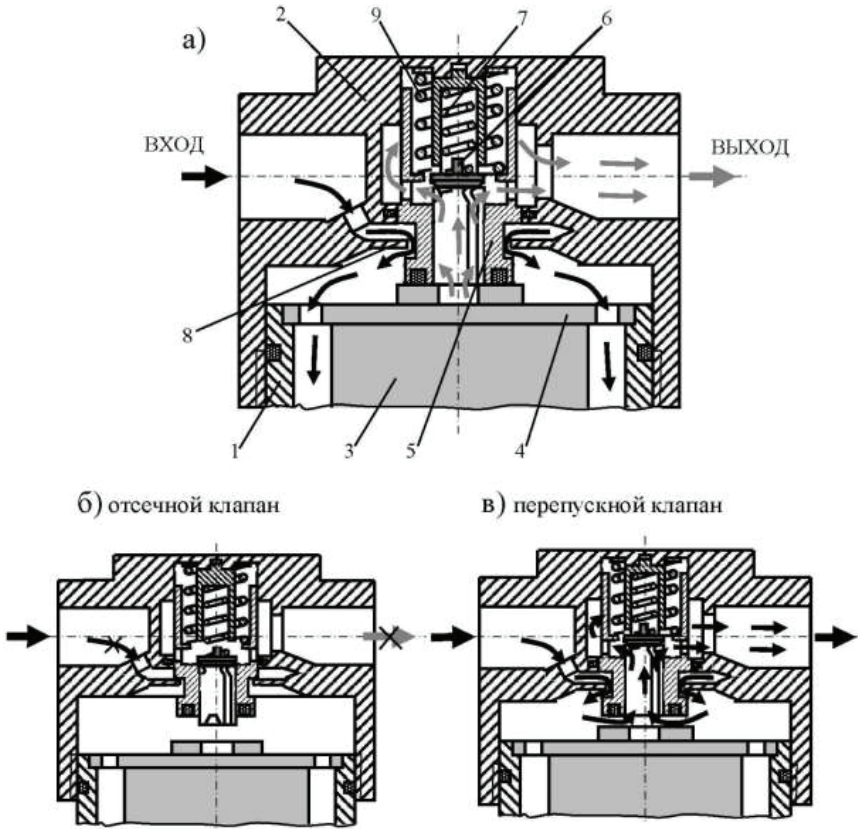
Гидравлический фильтр, где 1- стакан; 2- крышка; 3- фильтроэлемент; 4- фланец; 5- перепускной клапан; 6- отсечной клапан; 7,9- пружина; 8- седло
